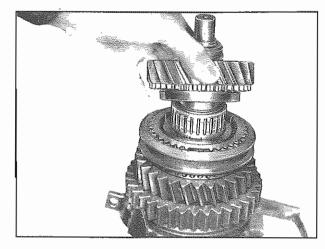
Ingranaggio della 2a marcia 2nd gear
